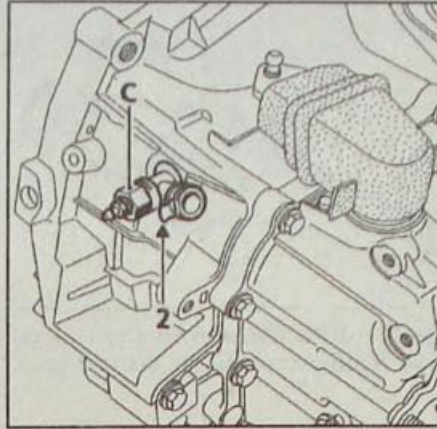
Расположение фиксатора (2) установленного на штуцере (С) рабочего цилиндра сцепления
